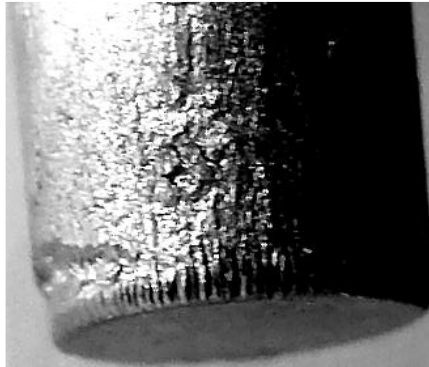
Знос пуансону штампа для виготовлення неметалевого одноразового абразивного інструменту по боковій поверхні.
